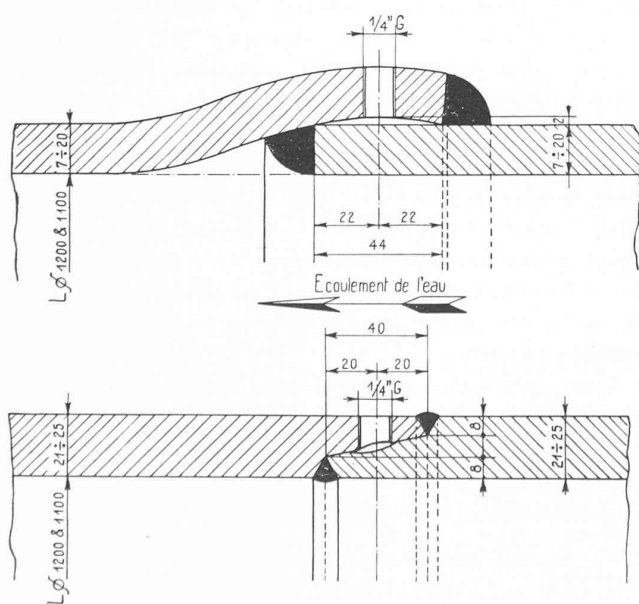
Assemblage des tuyaux de la conduite forcée d'Orsières, à 2 lignes de soudure, suivant le brevet Sulzer.
